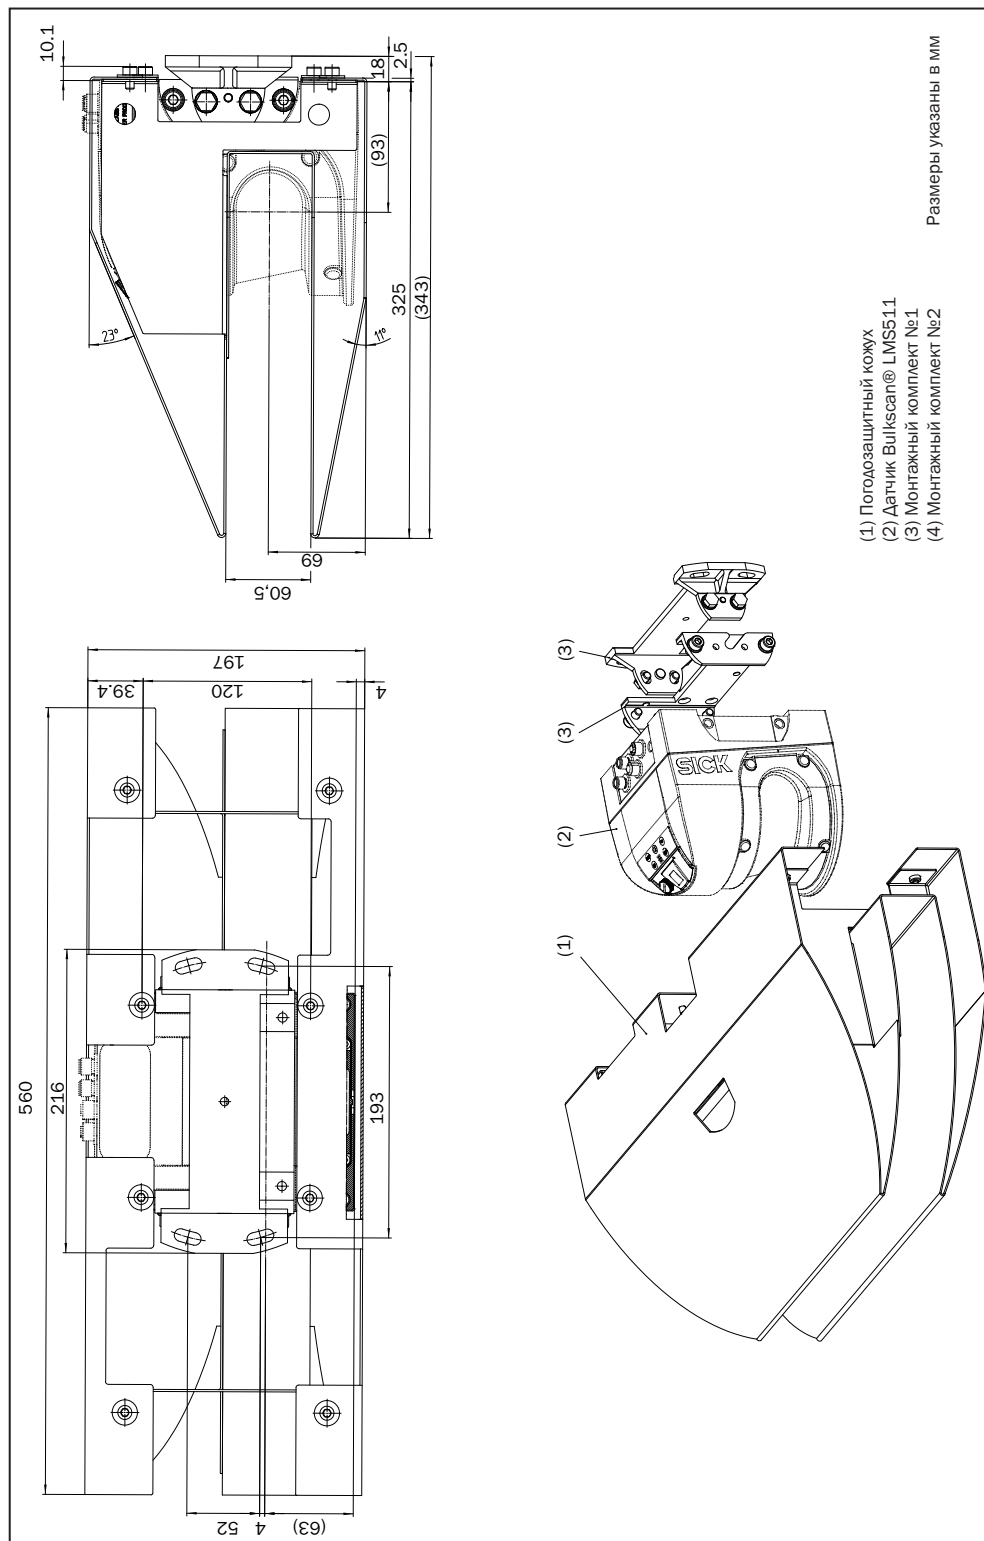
Размерный чертёж погодозащитного кожуха (Артикул 2063050)
